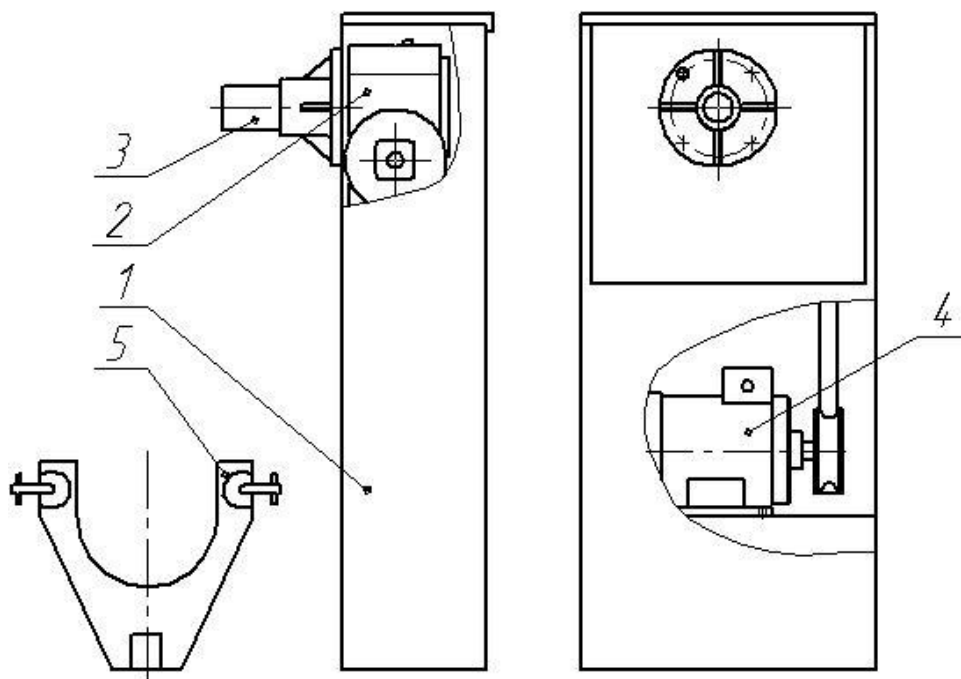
Схема стенда для разборки и сборки редукторов задних мостов автомобилей ЗИЛ и КамАЗ модель Р-640
